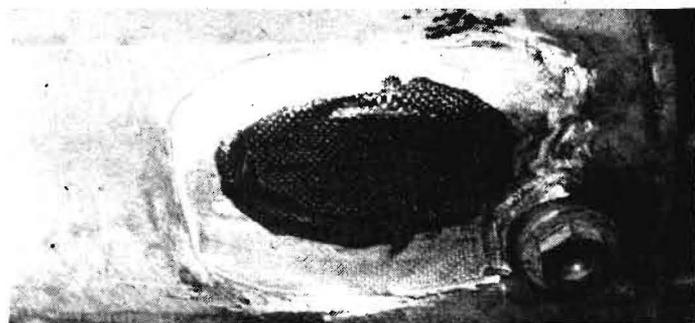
Mit Hilfe der Laminieretechnik instand gesetztes Getriebegehäuse
